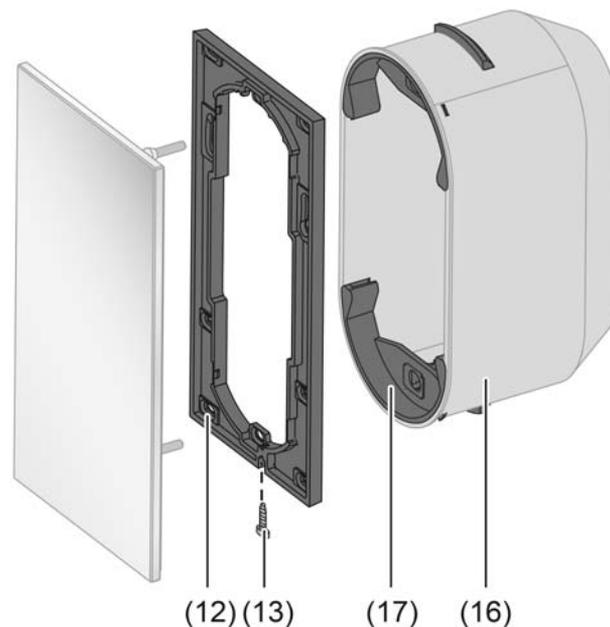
Gerätemontage eines Glas-Sensors TS Komfort mit erhöhtem Demontageschutz
